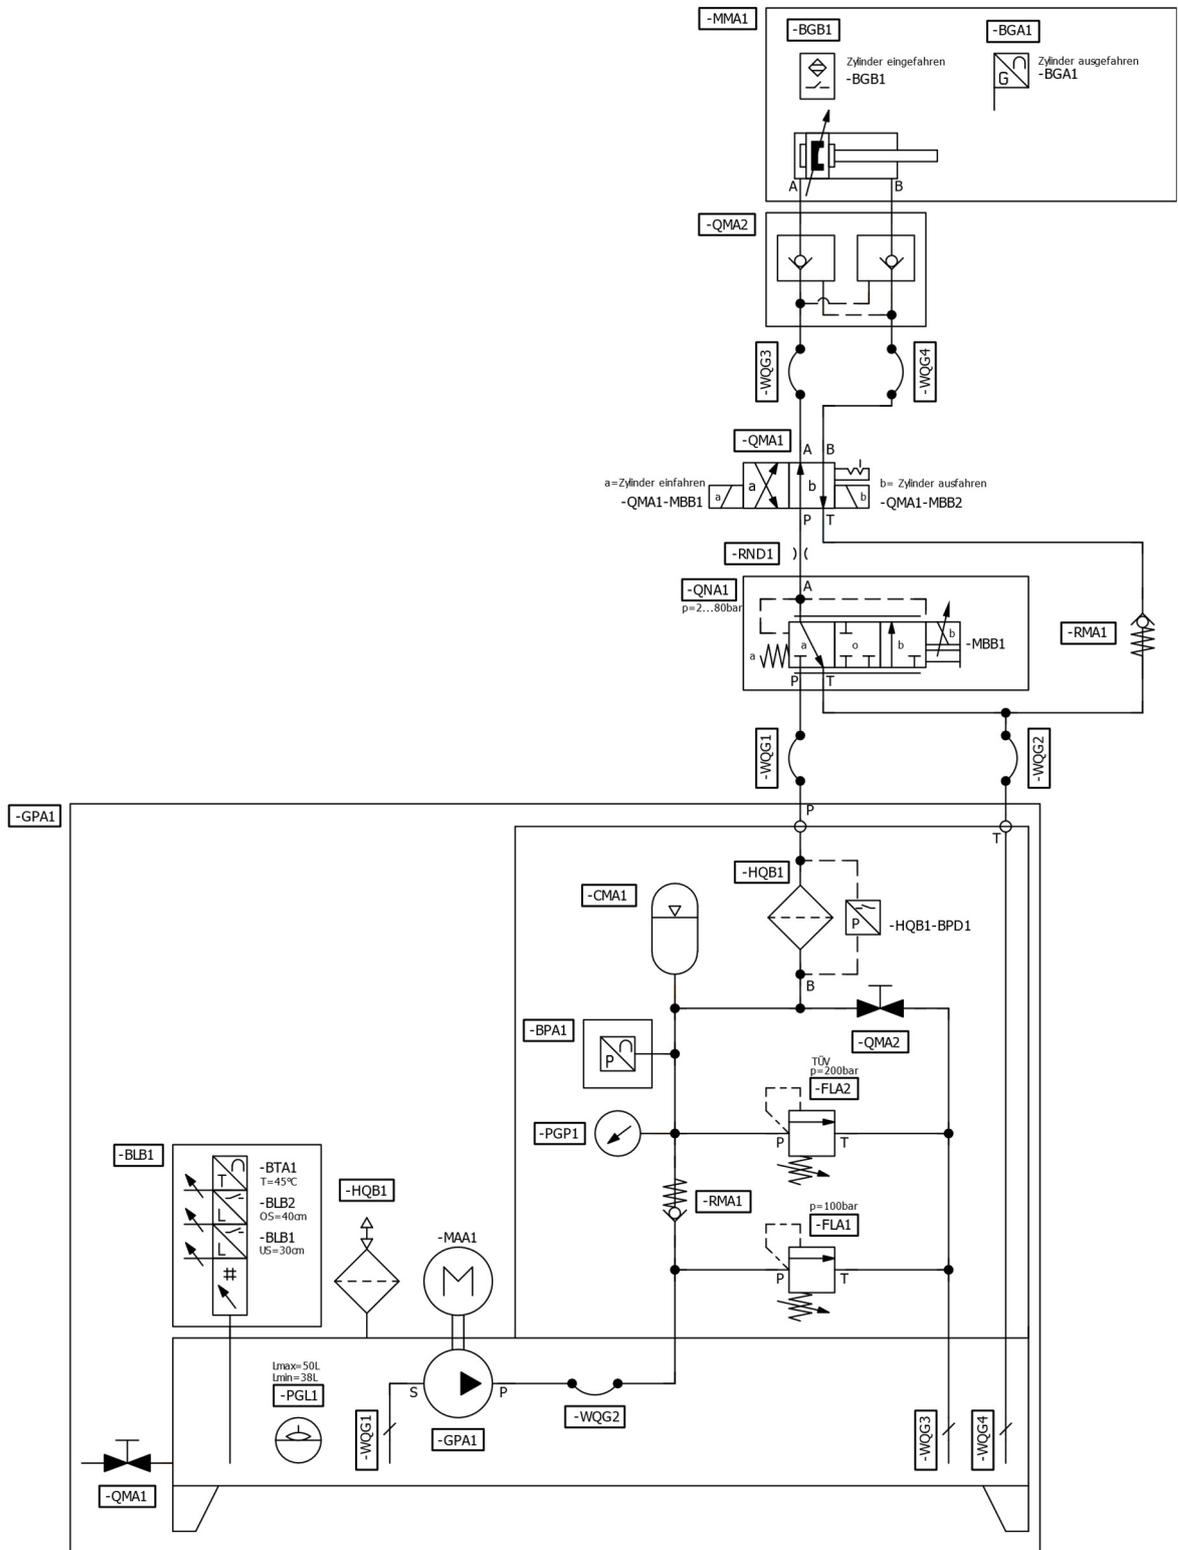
Beispiel für die Kennzeichnung hydraulischer Betriebsmittel
